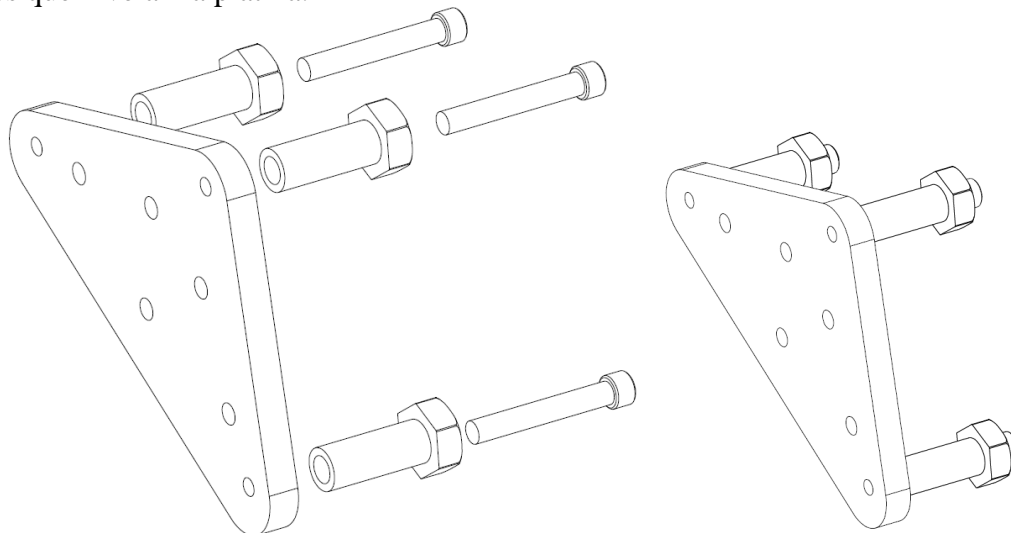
Mecanismo nivelador de la platina. Cada platina consta de 3 pares de tornillos coaxiales para modificar su altura. a) Vista explosionada de platina y tornillos (izquierda). b) Platina y tornillos en ensamble (derecha).
